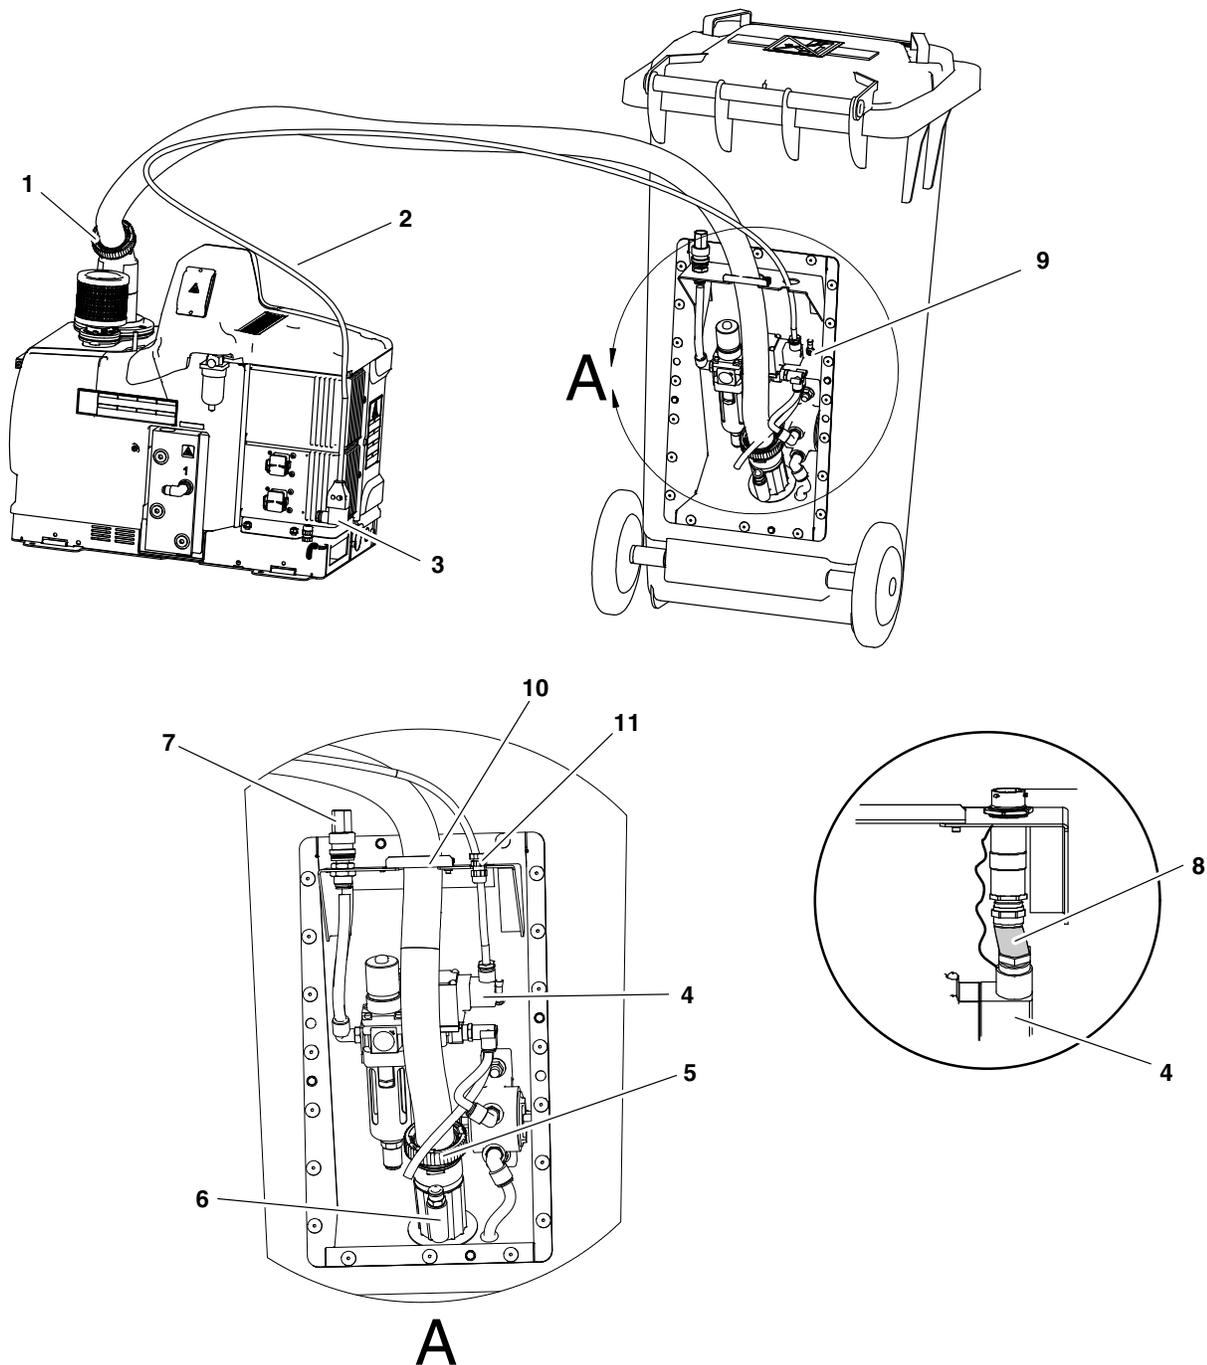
Realizzare i collegamenti del cablaggio dell'elettrovalvola e del tubo di trasferimento per un bidone ad alimentazione singola
